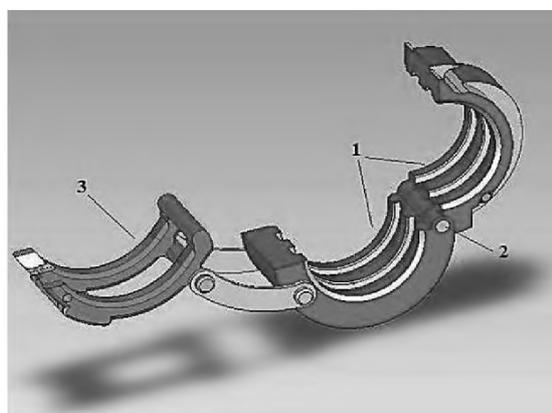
Крепежное устройство для зажима каркаса напорного рукава на втулке соединительной головки
